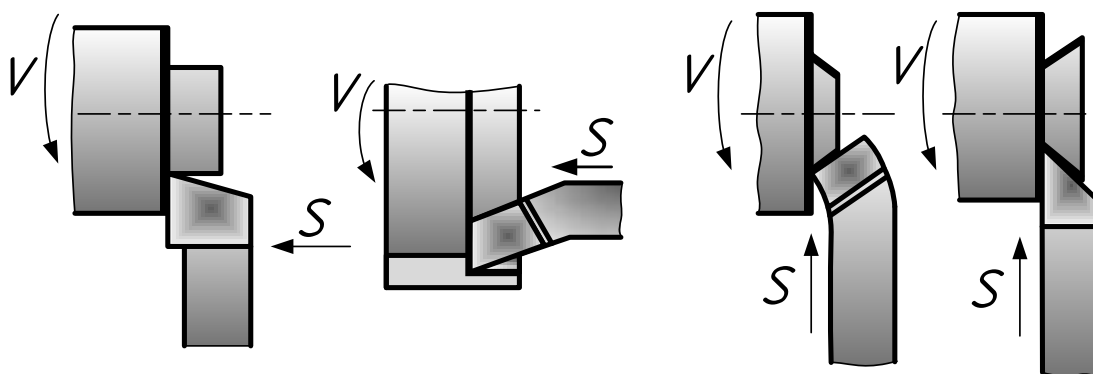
Обработка упорными проходными и подрезными токарными резцами
